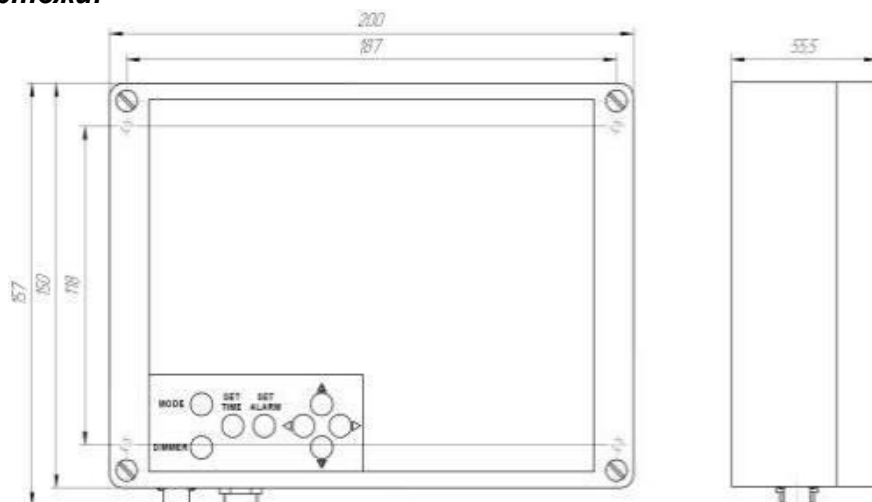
Габаритный чертеж ИПСС-00, ИПСС-01
